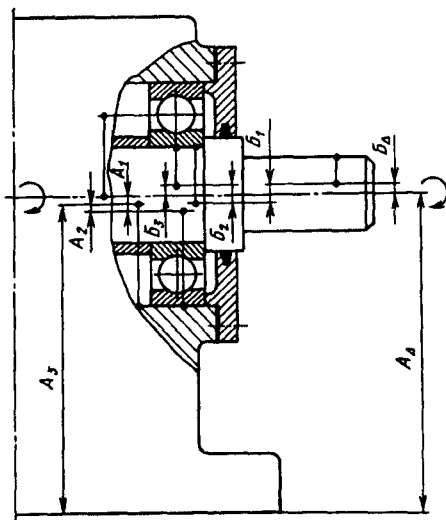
Размерные цепи для размерного анализа конструкции
